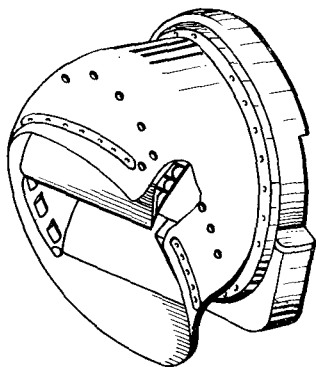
Поворотное сопло двигателя «Пегас» с двумя направляющими лопатками
